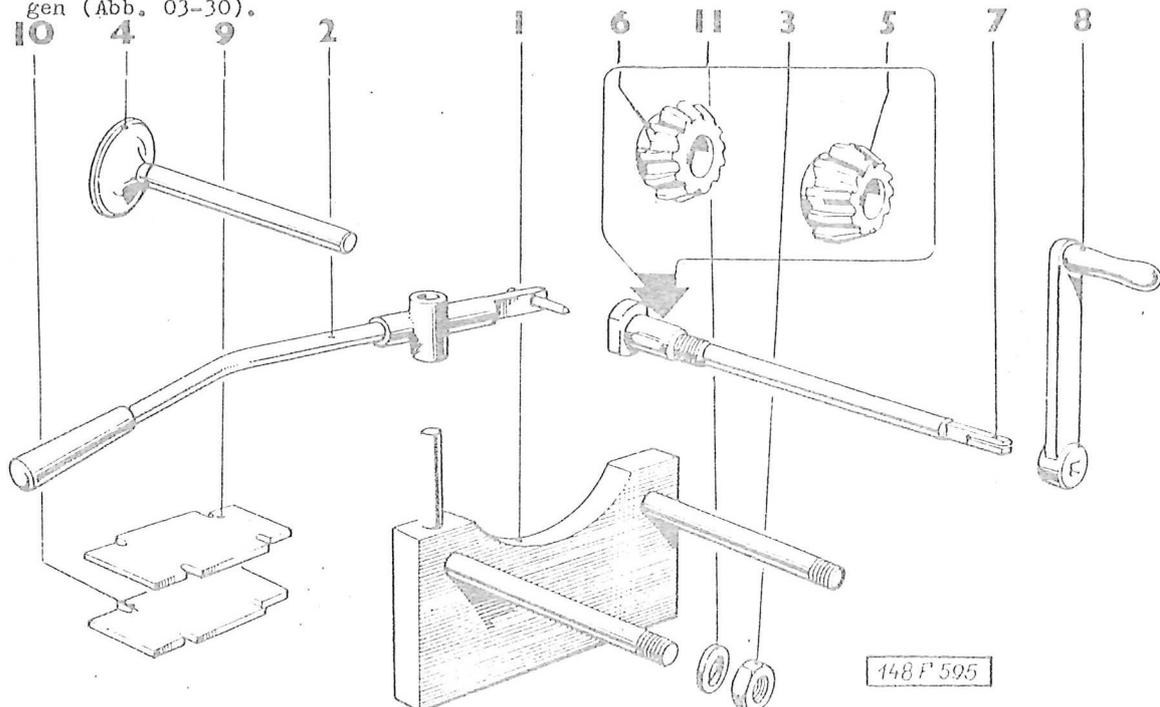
Behelfsmittel für die Bearbeitung der Ventilsitze
